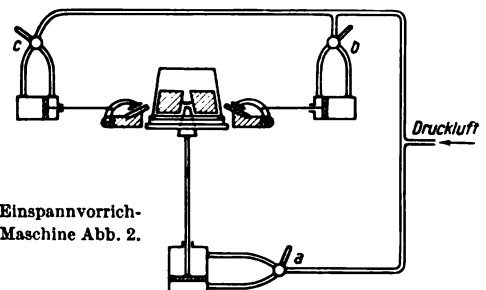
Einspannvorrichtung der Maschine Abb. 2.
